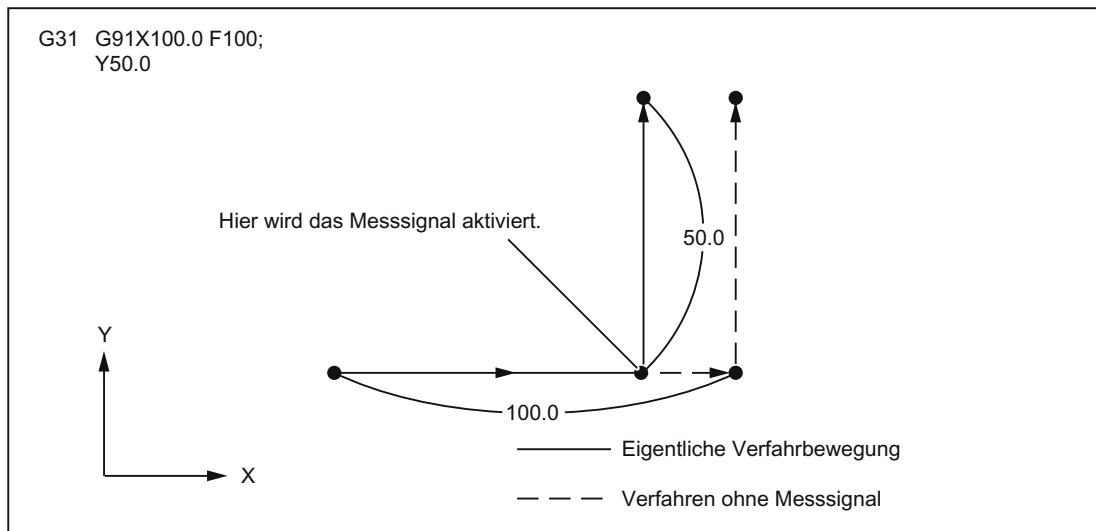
G31 mit inkrementeller Positionsangabe für eine Achse
